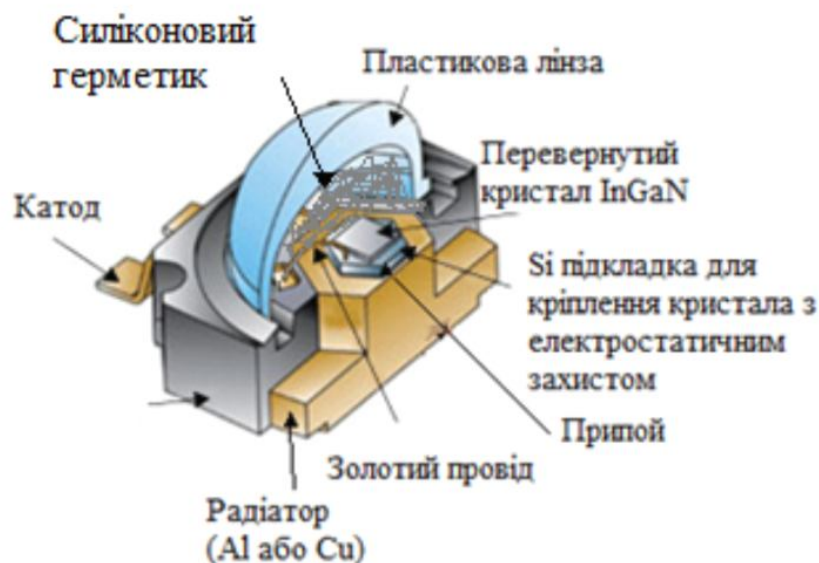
Конструкція SMD-корпуса потужного СД з перевернутим кристалом
